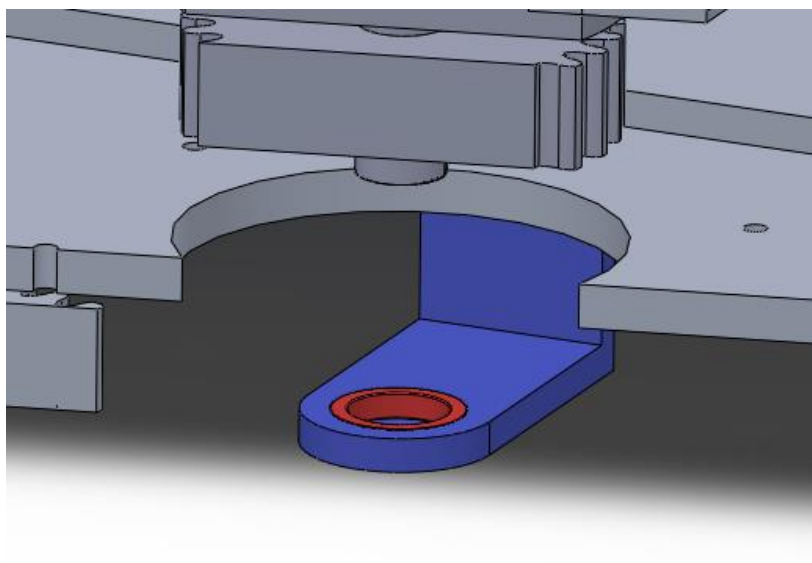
Posicionamiento del rodamiento inferior (Vista explosionada).
